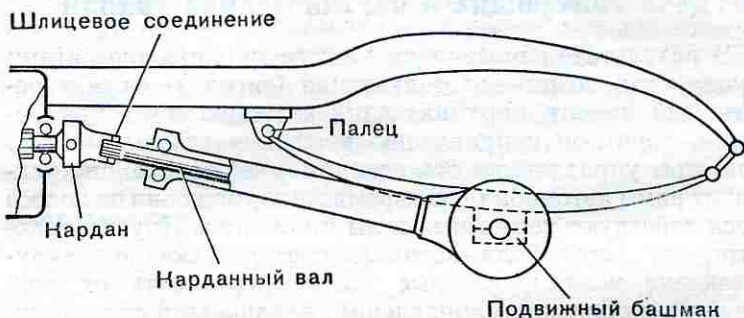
Передача толкающих и скручивающих усилий рессорами (закрытая карданная передача)
